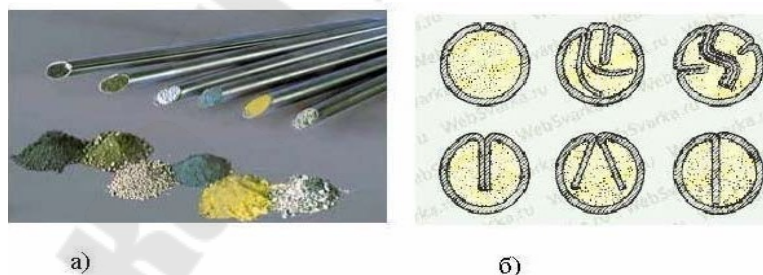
Порошковые проволоки для сварки и наплавки: а – внешний вид; б – сечения проволоки
